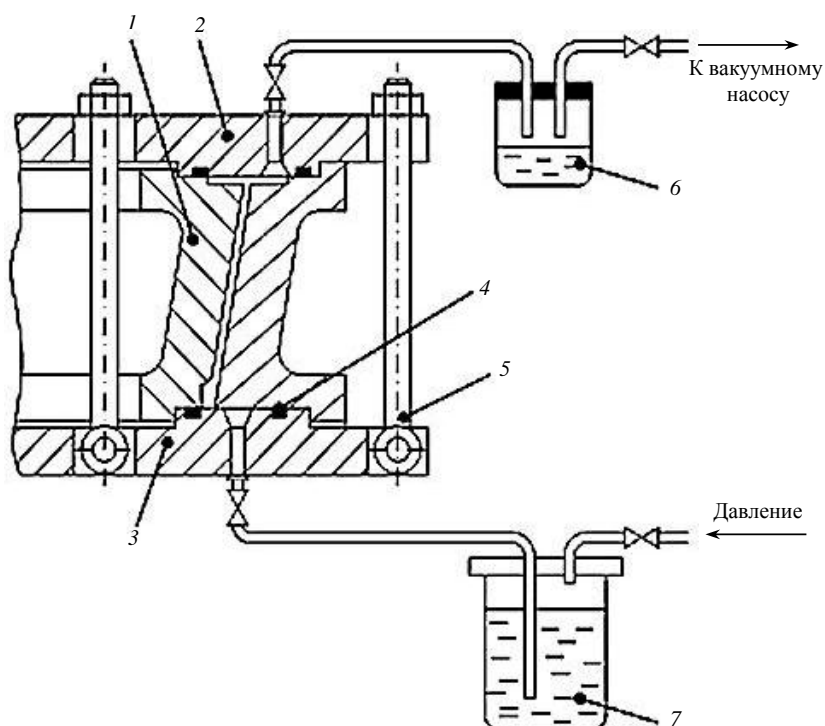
Схема изготовления деталей пропиткой под вакуумом и давлением:
